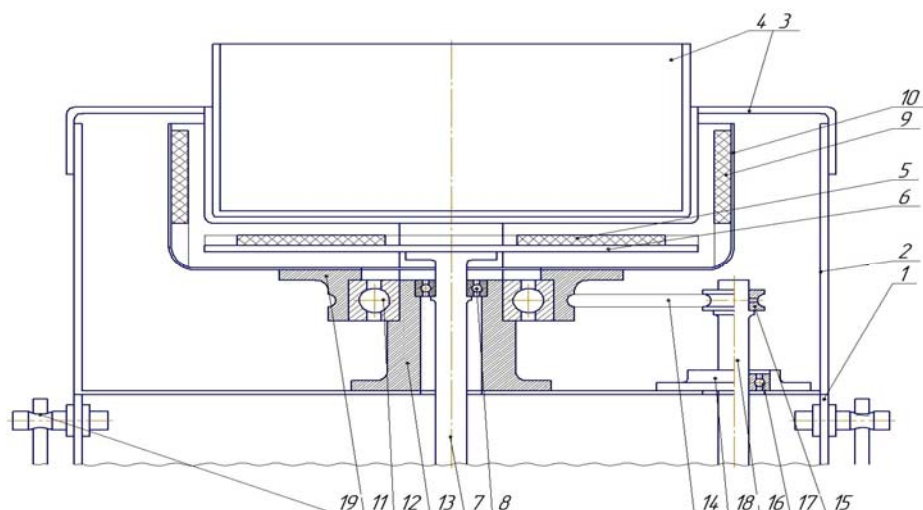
Установка для магнитной галтовки: 1 – основной корпус; 2 – верхняя часть корпуса; 3 – рабочий объем; 4 – рабочий контейнер; 5 – основная группа постоянных магнитов; 6 – подвижный диск; 7 – основной вал; 8 – подшипник; 9 – постоянные магниты; 10 – подвижный борт; 11 – втулка №1; 12 – основной подшипник; 13 – втулка №2; 14 – ремень; 15 – блок; 16 – вспомогательный вал; 17 – подшипник; 18 – втулка №3; 19 – поворотный механизм
